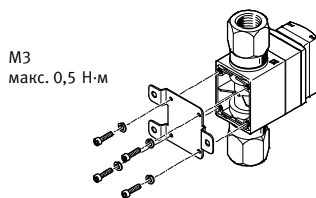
Монтаж на стену (SFAW-...-W-...):
